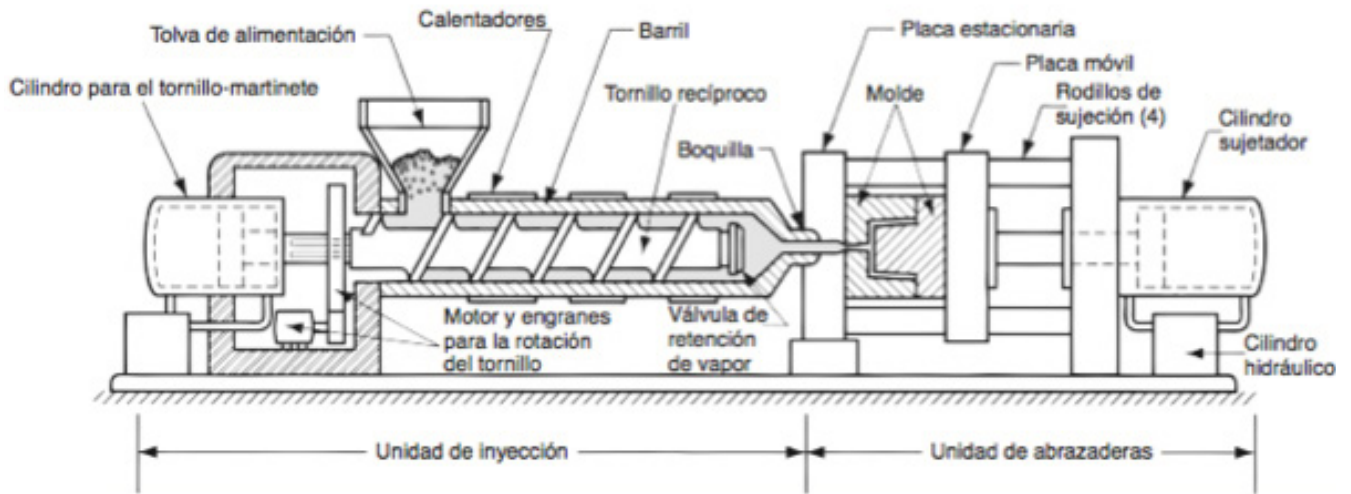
Componentes de una máquina de moldeo por inyección.
